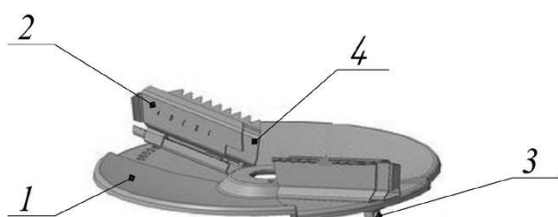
Метатель (рассеивающий диск): 1 – диск; 2 – лопатка; 3 – фиксатор; 4 – направляющая
